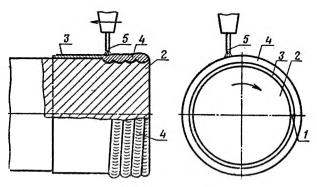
Схема наплавки шейки вала по металлической оболочке:
